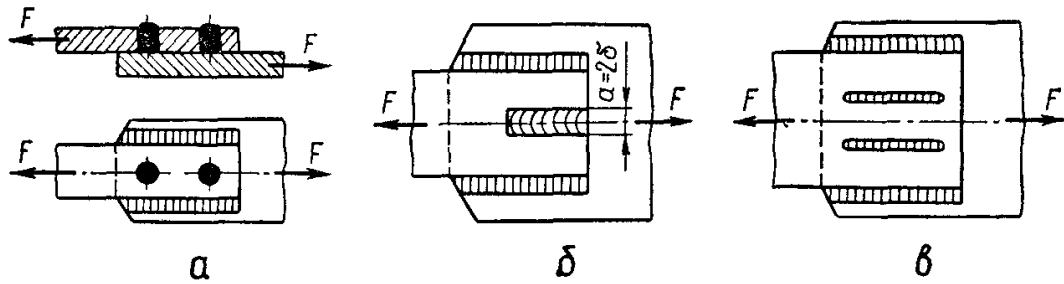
Коркові, прорізні та проплавні зварні шви
